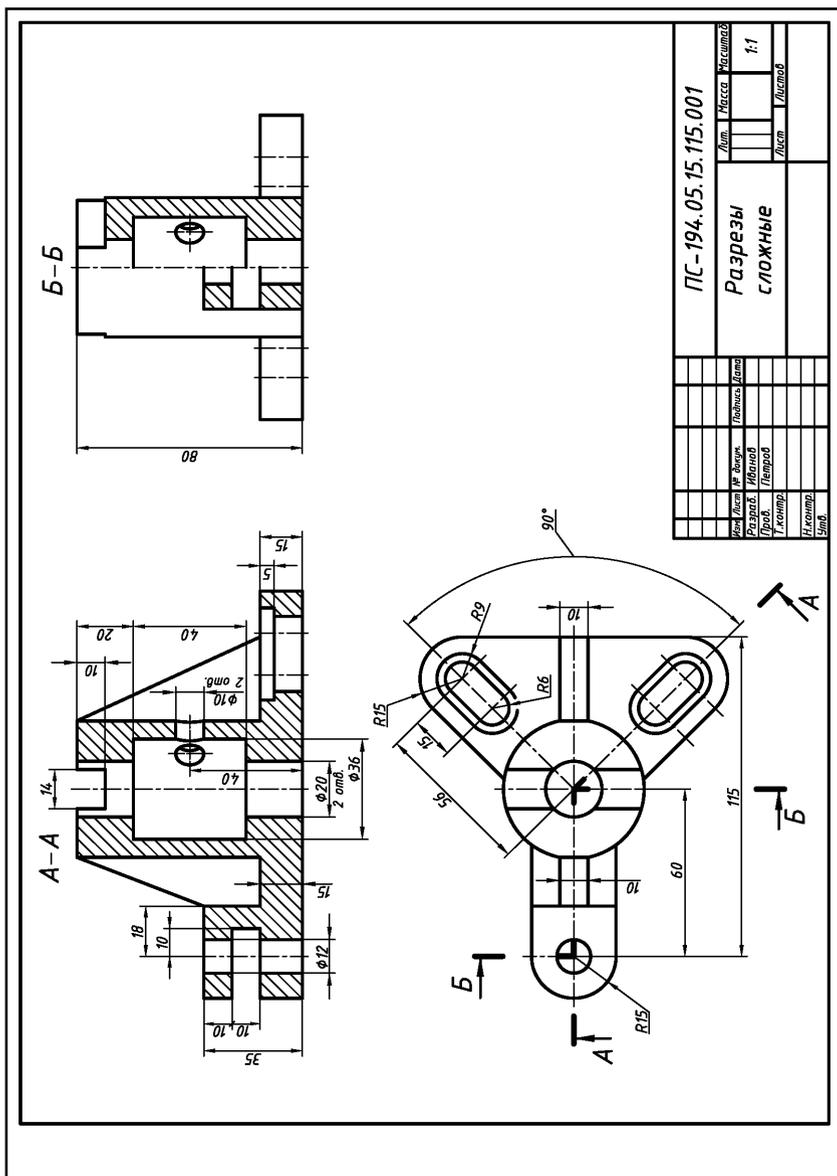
Пример оформления чертежа детали со сложными разрезами (вариант исходной заготовки – рис. 1.37)
